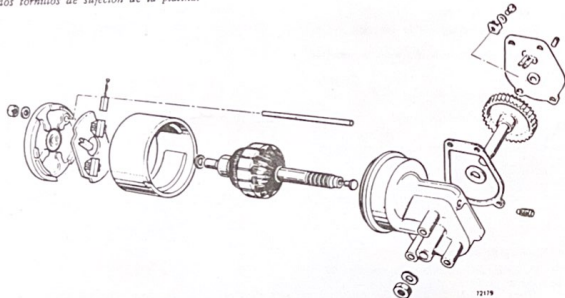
Despiece del motor de limpiaparabrisas. SEV 116006.
